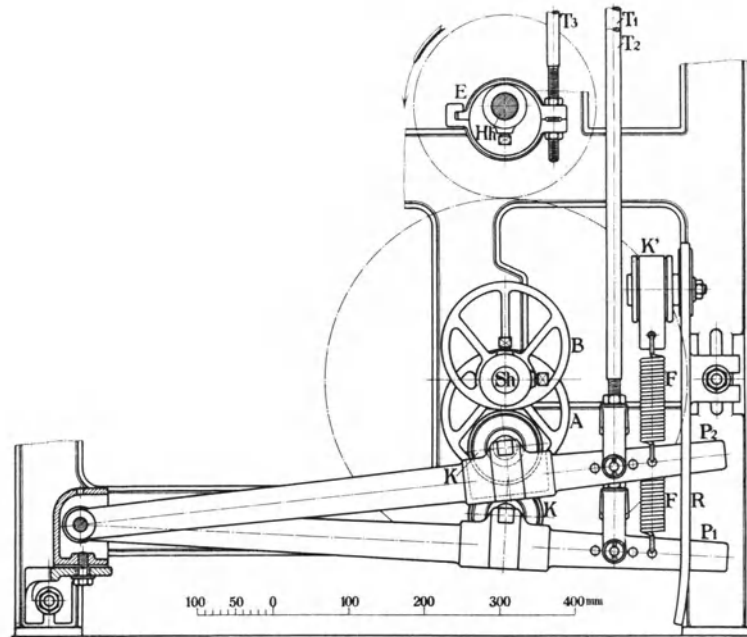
Antrieb der Hodgson'schen Schaftmaschine.
